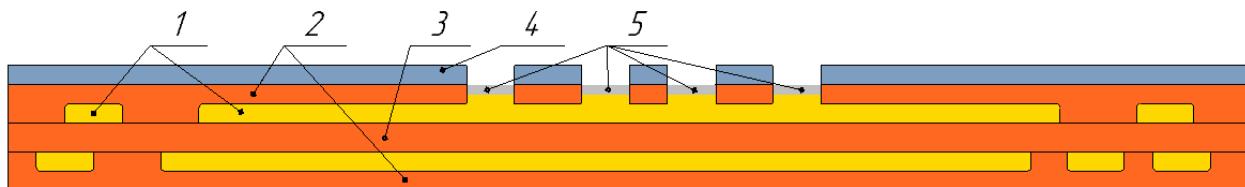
Нанесення металорезисту: 1 – мідна фольга; 2 – покривна плівка на основі полімеризованого поліімідного лаку; 3 – базовий поліімід; 4 – фоторезист; 5 – металорезист
